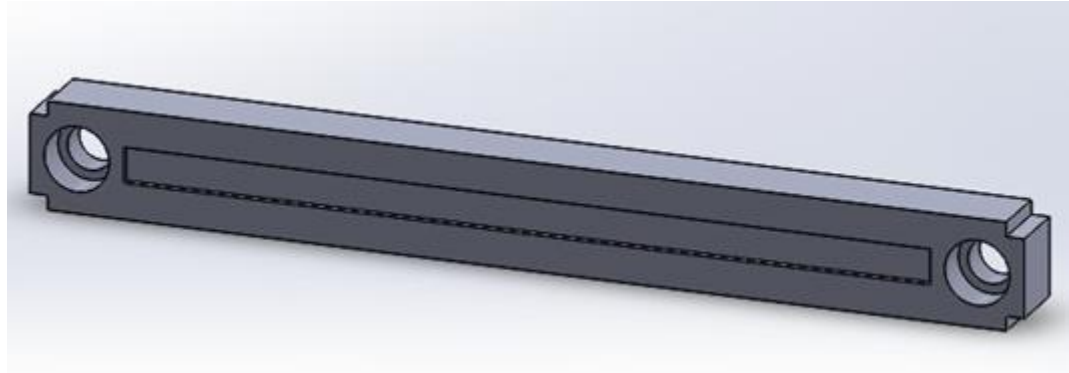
Y 60: diseño y dimensiones de base de molde hembra.
